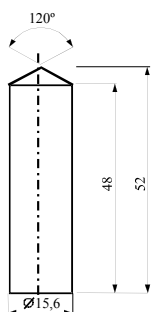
Êmbolo cilíndrico de bronze, dimensões em mm
